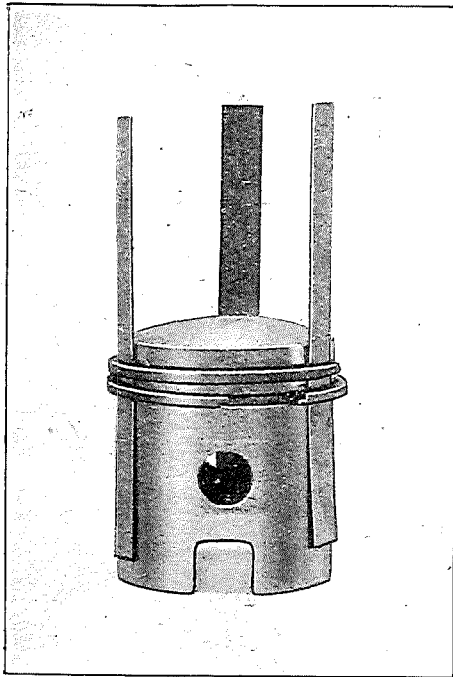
Entfernen u. Aufziehen der Kolbenringe
